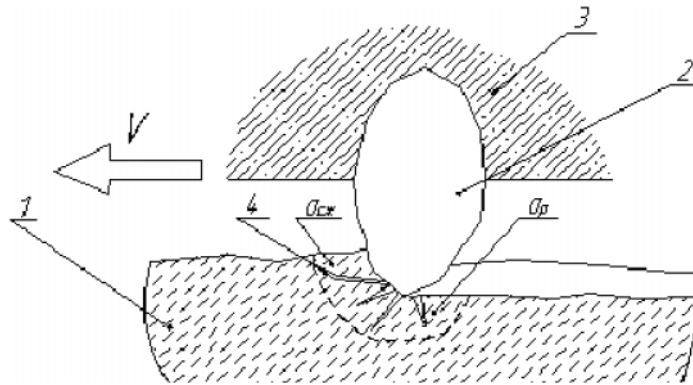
Розташування мікротріщин при шліфуванні поверхні заготовок з каменя
